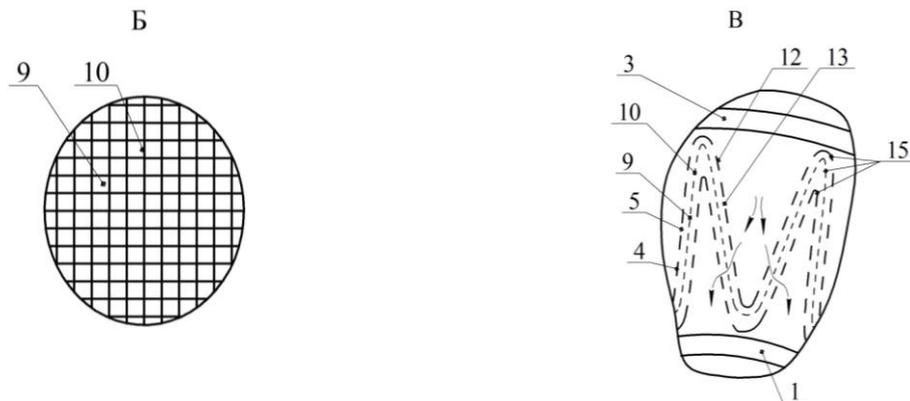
Фрагменты конструкции по предотвращению разрушения фильтрующего элемента газового цилиндрического фильтра
